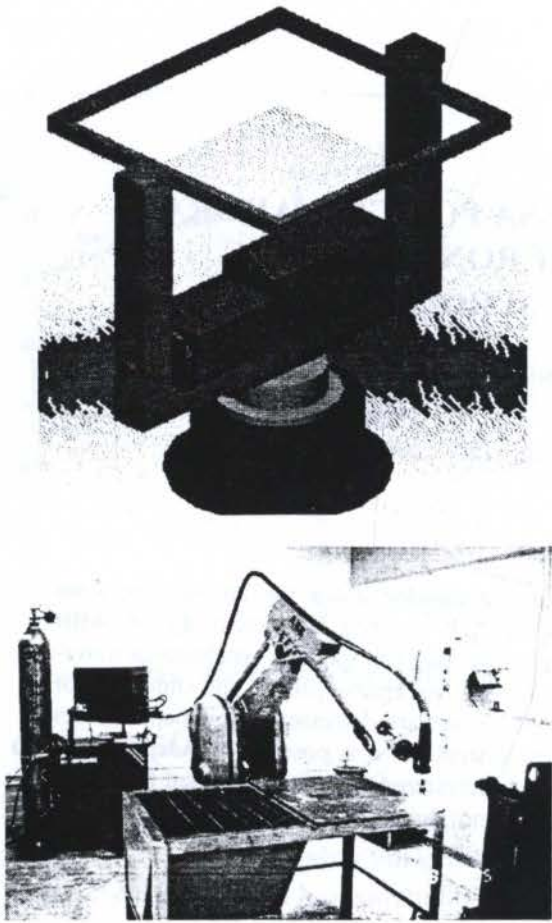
Mesa Posicionadora e Célula de Soldagem - Laboratório GRACO/UnB.
